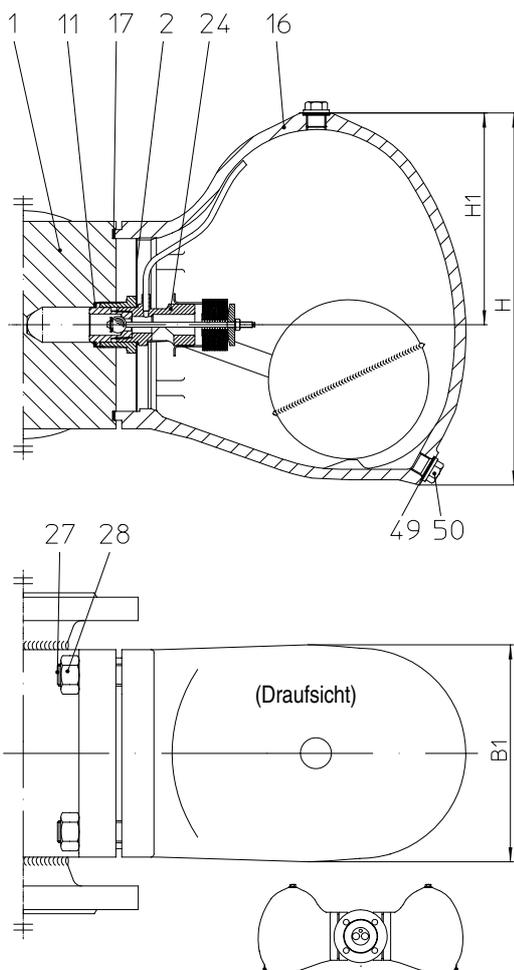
1 mit Flanschen - horizontale Einbaulage
